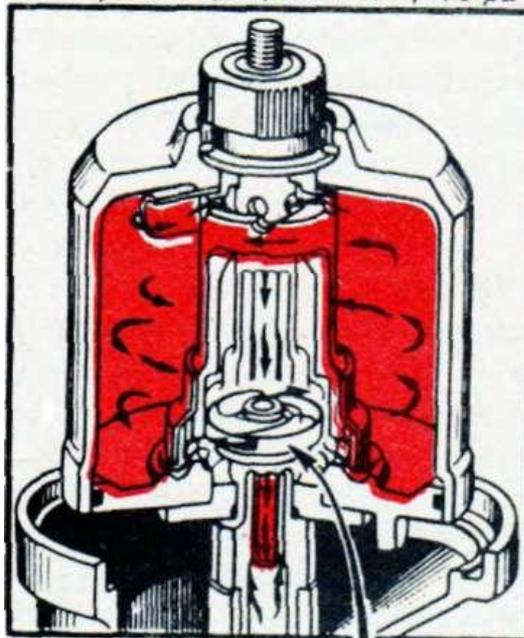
Центробежный масляный фильтр: 1 - корпус; 2 - колпак ротора; 3-ротор; 4- колпак фильтра; 5 - гайка крепления колпака ротора; 6 - подшипник шариковый упорный; 7 - шайба упорная; 8 - гайка крепления ротора; 9 - гайка крепления колпака фильтра; 10 - втулка верхняя ротора; 11 - ось ротора; 12 - экран; 13 - втулка нижняя ротора; 14 - палец стопора; 15 - пластина стопора; 16 - пружина стопора; 17 - трубка отвода масла
